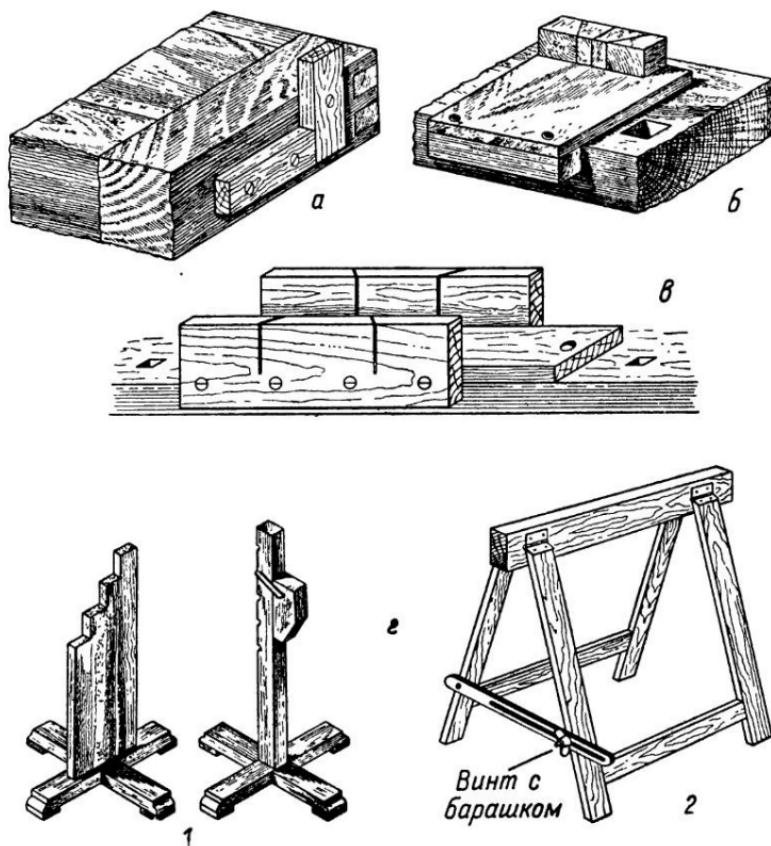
Приспособления к верстаку: *a* — упор; *b* — подкладка с упором; *c* — распиловочный ящик; *d* — служки; *1* — для строжки кромок; *2* — для строжки пластей.
